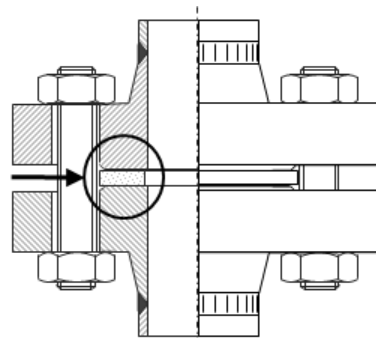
schraubentechnisch ungünstiges System Flanschverbindung
